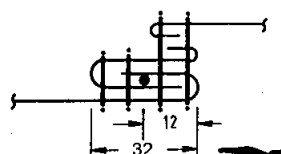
Rechteckiger Flicker kreuzt Quernaht
